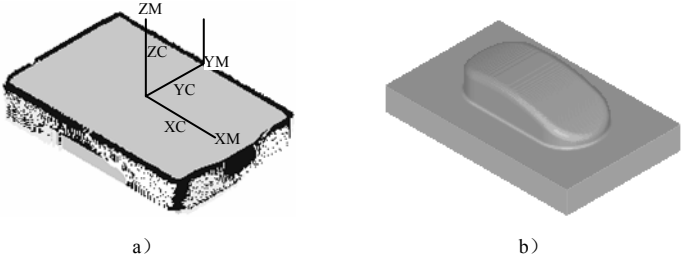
型腔铣粗加工的“刀具路径”和“实体切削验证”
